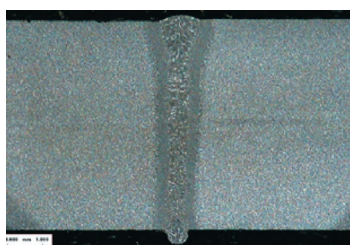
Образец лазерной сварки с глубоким проплавлением  $k = 4$ :  $P = 5,4$  кВт,  $V = 0,9$  м/мин,  $\delta = 12$  мм [5].
